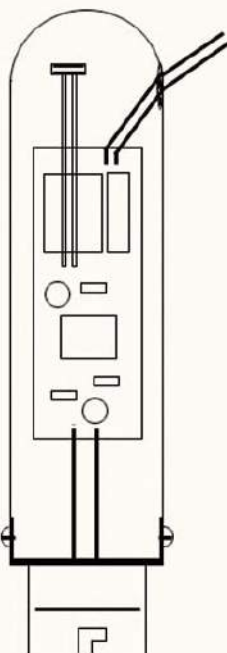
Projekt płytki PCB dla „smart bulb holder-a”
